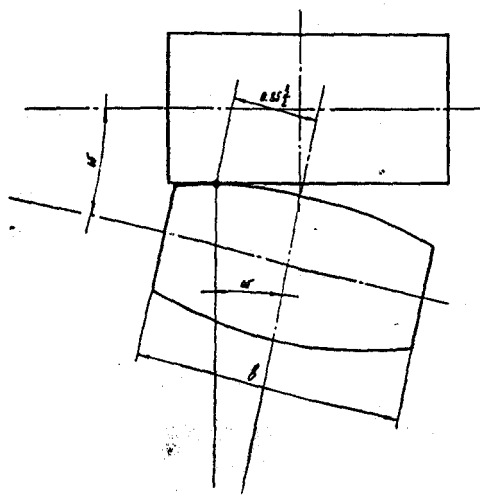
Схема контакта зубьев втулки и обоймы в зубчатой муфте: α – угол перехода осей соединяемых валов; b – длина зуба втулки.
